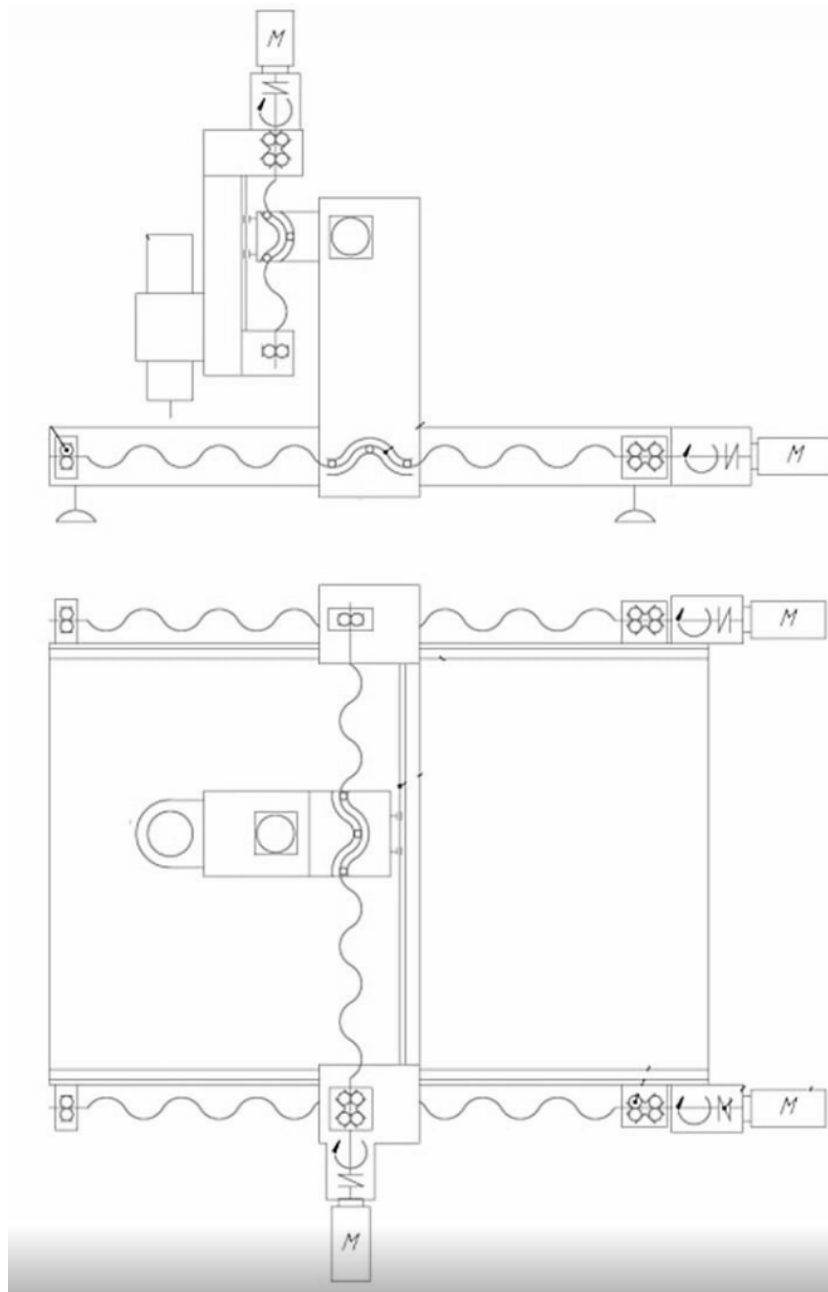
Кінематична схема верстату для лазерного гравірування
